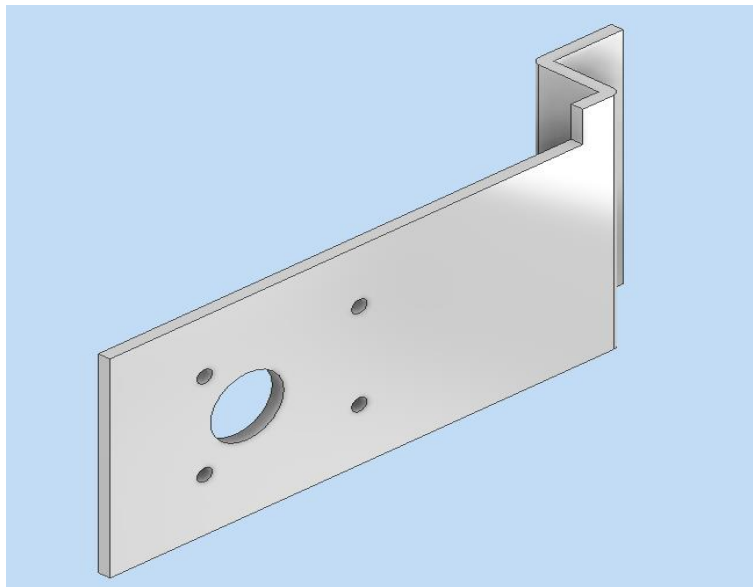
Soporte para el motorreductor diseñado en un CAD.
